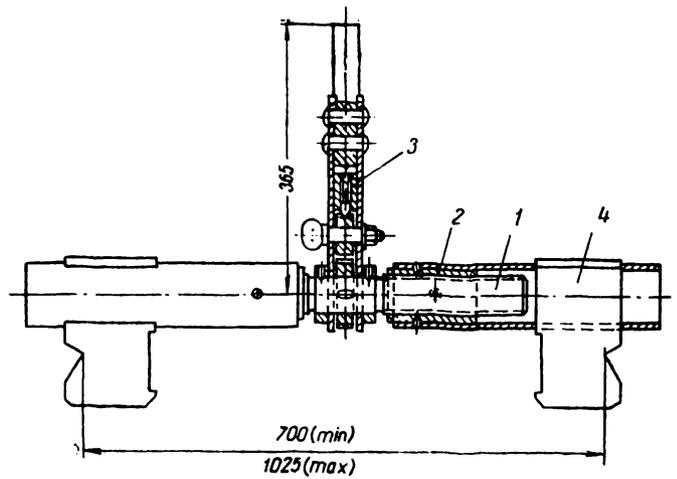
Приспособление для правки кузова вагонеток по обвязке
